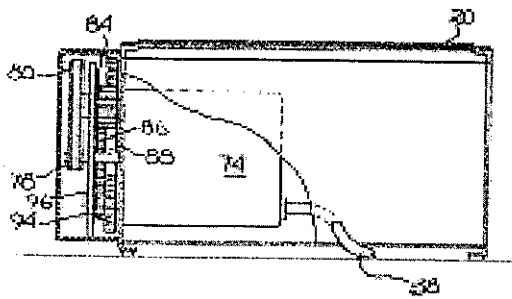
ลักษณะของเครื่อง Plastic Sheet Cleaning Machine
